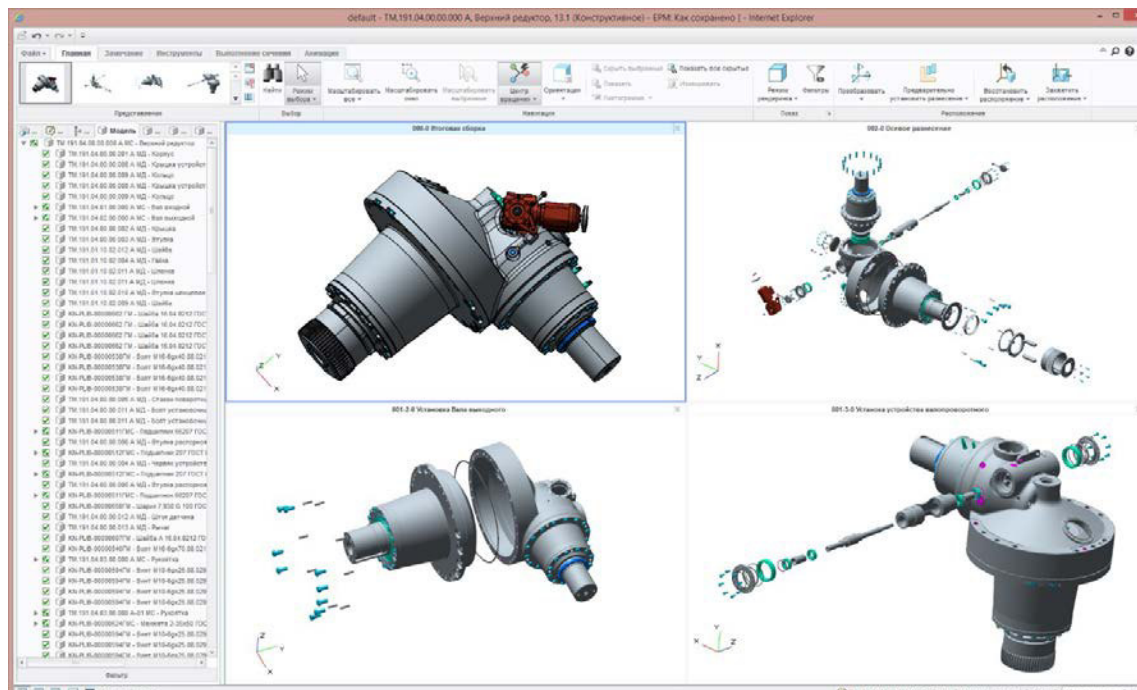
ИЭТР для сборки винторулевой колонки в CAD-системе Creo View под управлением PLM-системы Windchill
